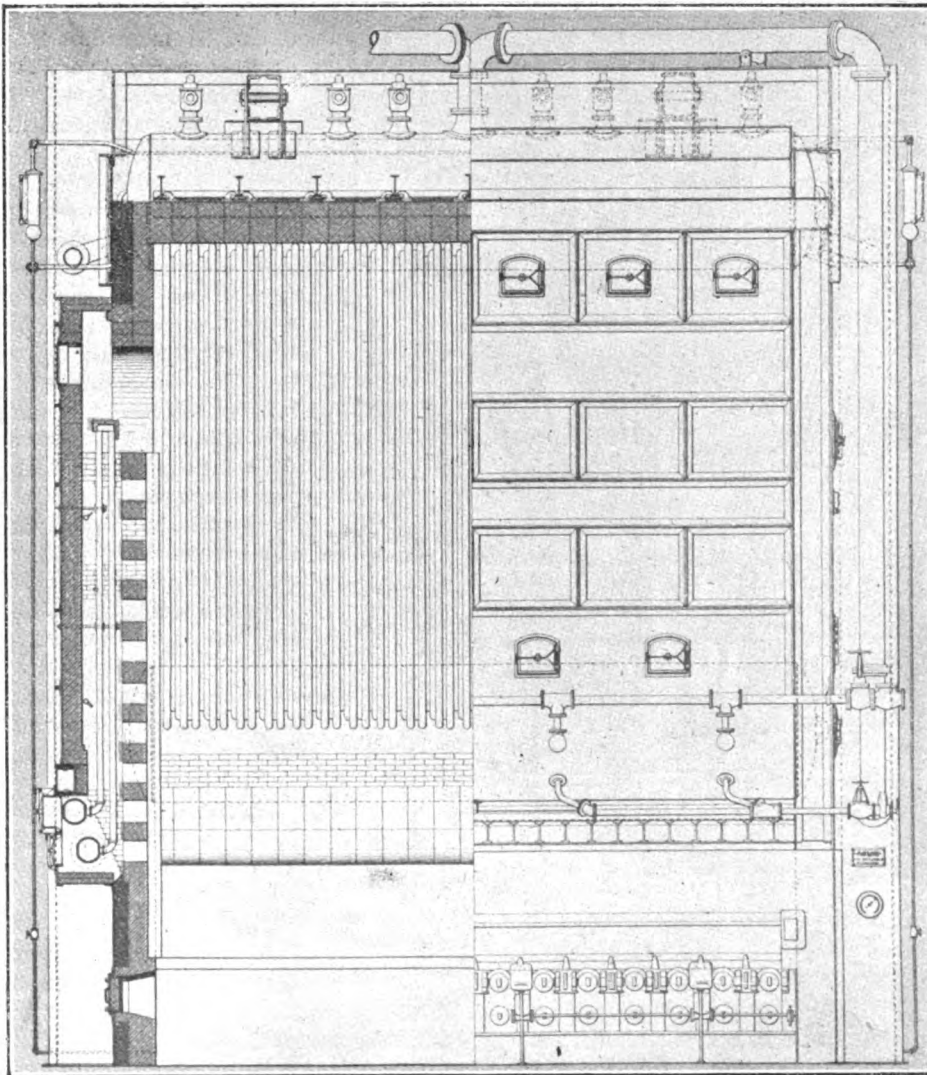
Chaudière Ladd-Belleville avec foyer mécanique et surchauffeur en façade.
